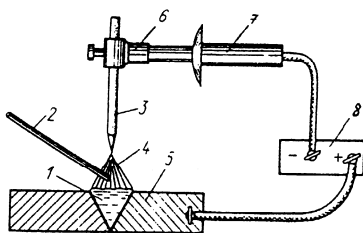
Схема зварювання з електродом, що не плавиться
